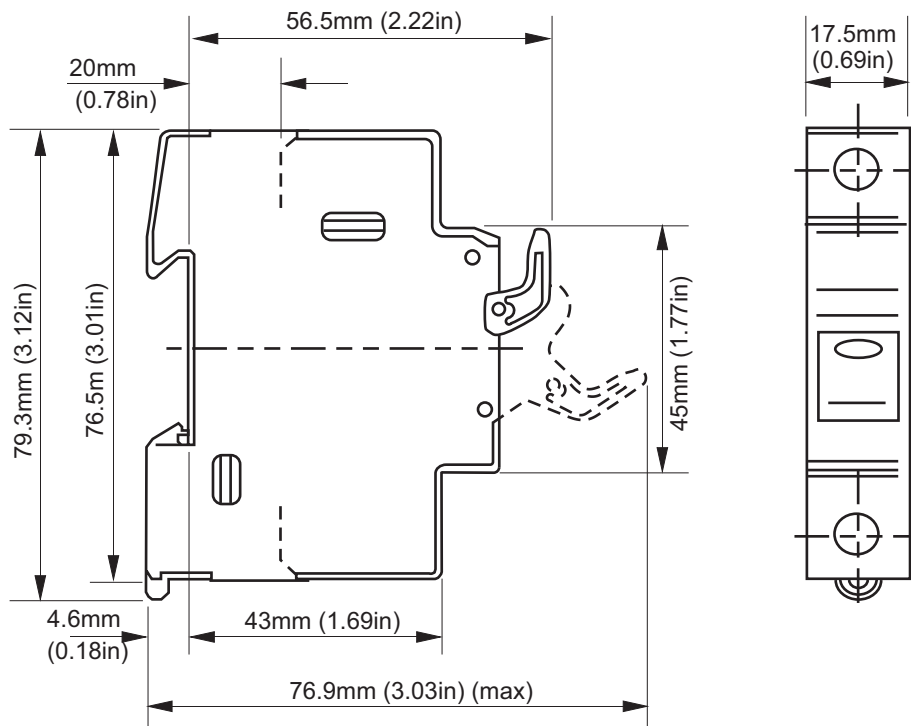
Las dimensiones del portafusibles: CUS101 (10x38 mm)
